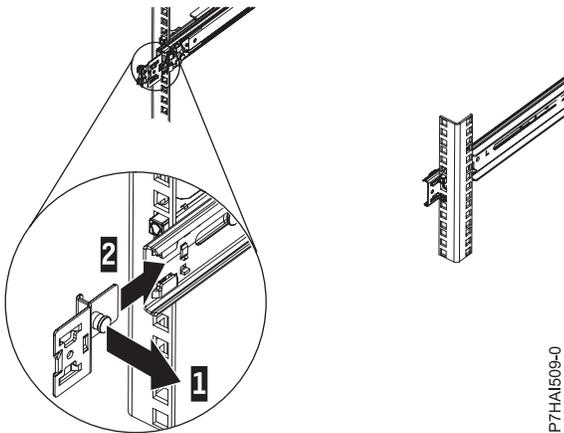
Patilla de pieza de sujeción de montaje extendida y pieza de sujeción de montaje instalada en el riel deslizante
